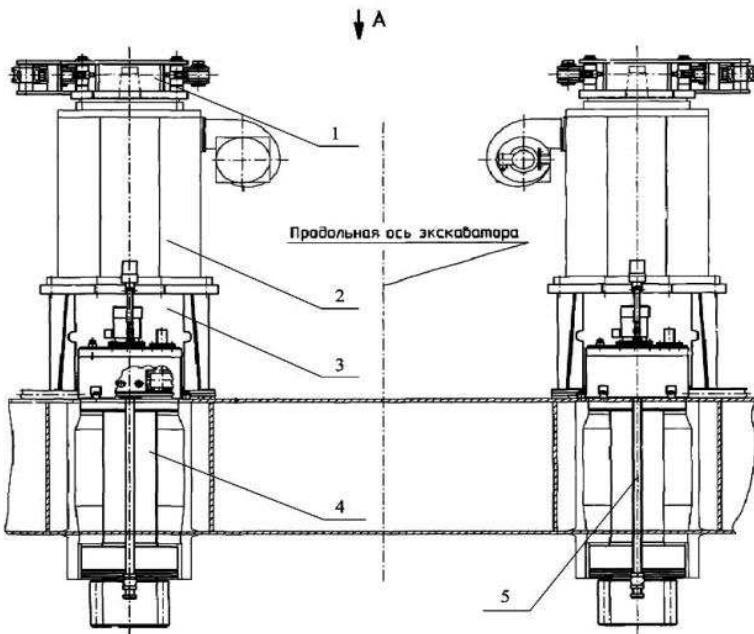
Привод механизма поворота (вид сбоку)
